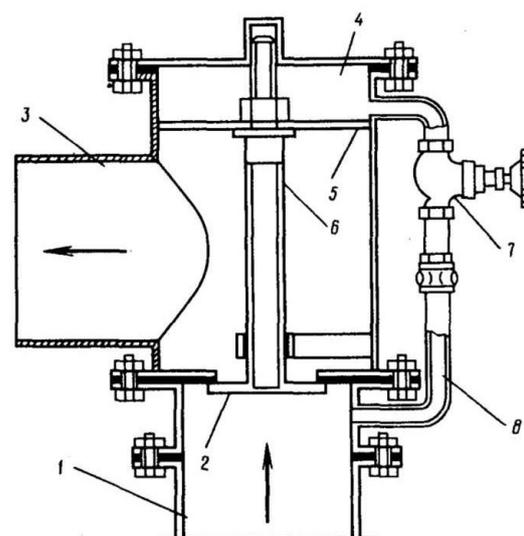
Схема работы клапана с гидроприводом: 1 — напорный трубопровод; 2 — клапан; 3 — трубопровод; 4 — силовая камера; 5 — силовой клапан; 6 — стержень; 7 — кран; 8 — обводная трубка
